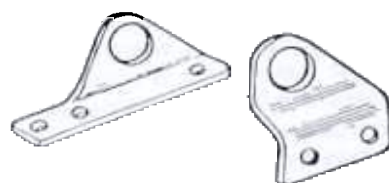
A-09-01 – Soportes de levantamiento del motor. Útil TTr/D 6004
